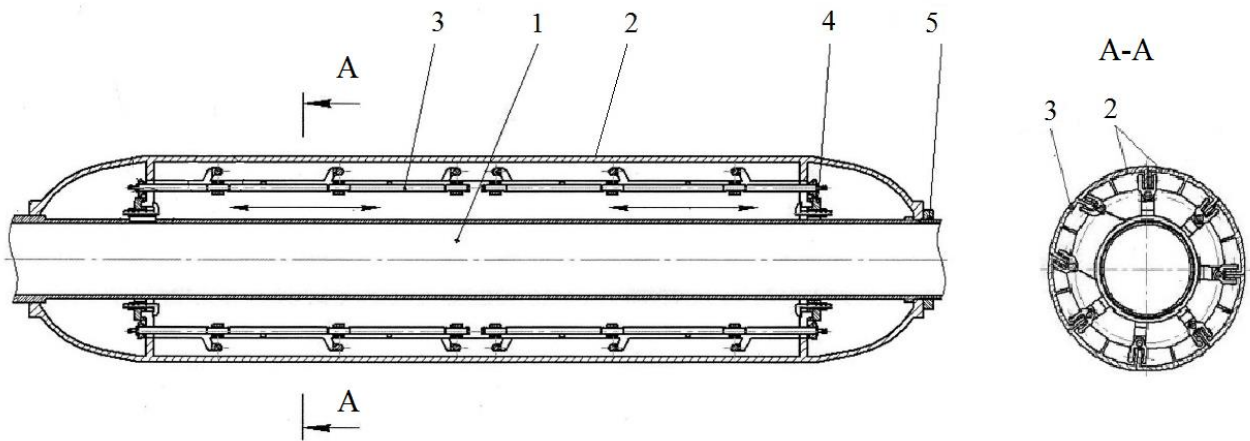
Конструктивная схема металлической разборной оправки с замковым устройством:
